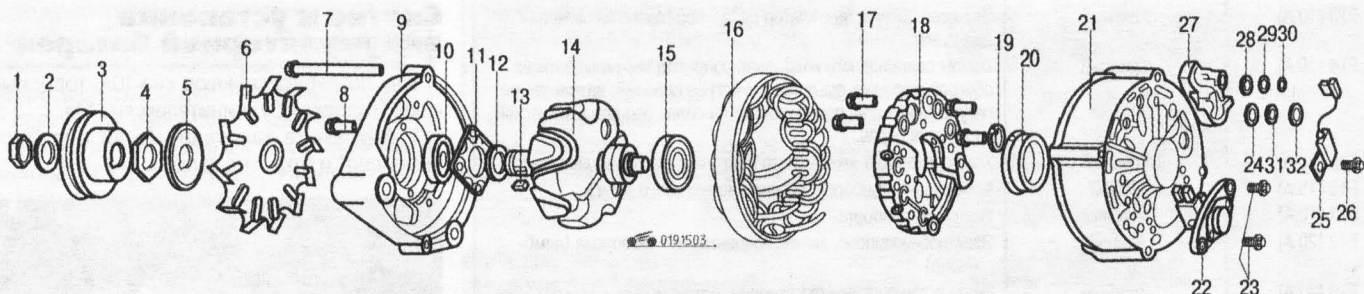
Генератор Bosch: 1, 29 – гайки; 2, 4, 12 – шайбы; 3 – шкив; 5 – дистанционная втулка; 6 – крыльчатка; 7, 8, 17, 23, 26 – винты; 9 – передняя крышка; 10 – подшипник; 11 – держатель подшипника; 13 – сегментная шпонка; 14 – ротор; 15 – подшипник; 16 – статор; 18 – блок выпрямительных диодов; 19 – втулка; 20 – пластмассовая втулка; 21 – задняя крышка; 22 – регулятор напряжения со щеточным узлом; 24, 31 – прокладки; 25 – конденсатор; 27 – изоляционная прокладка; 28, 30 – пружинные шайбы; 32 – прокладка
